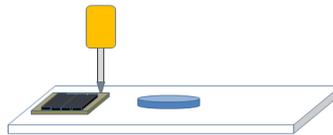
Fixando Suporte de Pilhas no Suporte de Madeira.
